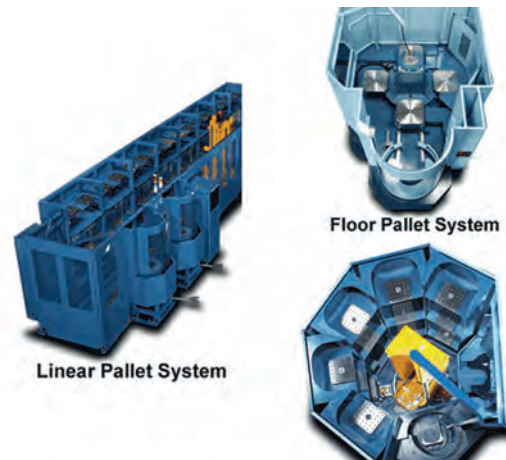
PALLET HANDLING PH50/20 firmy DMG
